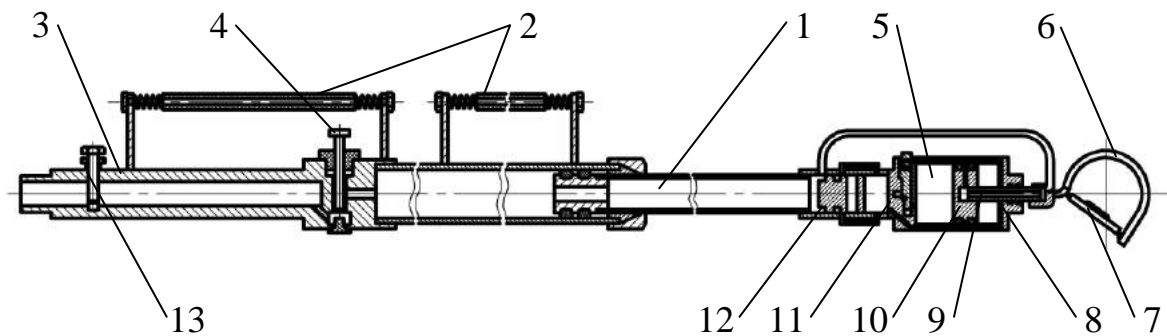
Схема ручного пневматичного струшувача плодів (а.с. № 1380663): 1 – телескопічна штанга; 2 – рукоятки; 3 – вхідний патрубков; 4 – клапан управління; 5 – пневматичний віброциліндр; 6 – гак; 7 – підтискний важіль; 8 – корпус віброциліндра; 9 – шток; 10 – поршень; 11 – золотник; 12 – клапан; 13 – регулятор швидкості (дросель)
